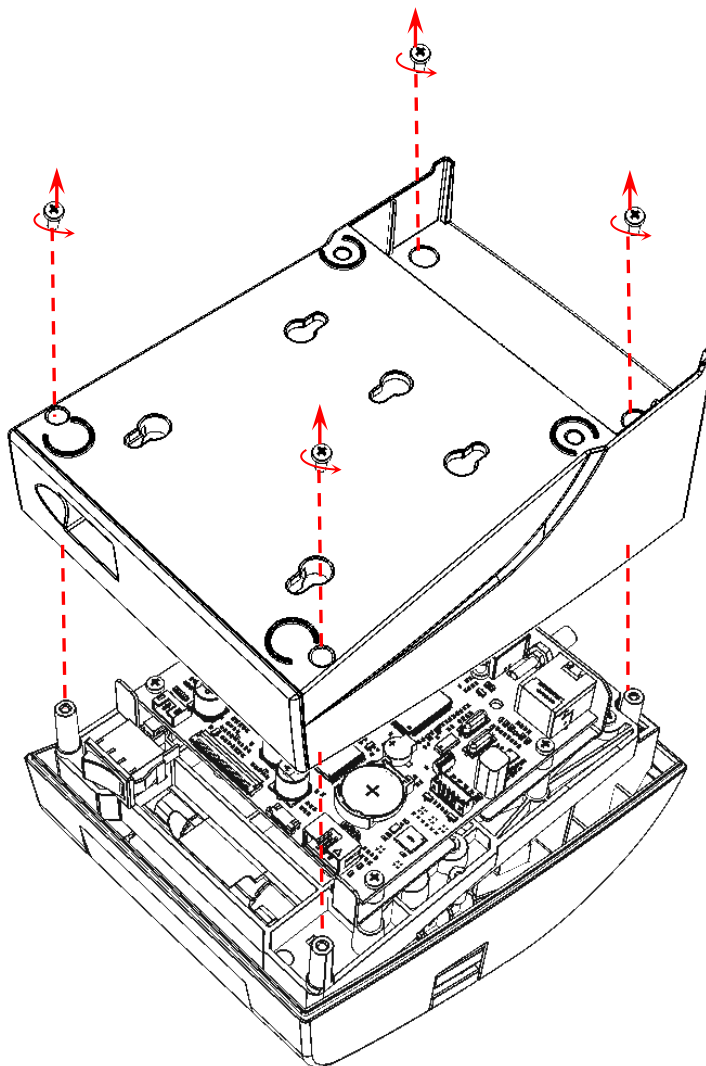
Демонтаж корпуса (отделение верхней части) (кабель ФН условно не показан)
